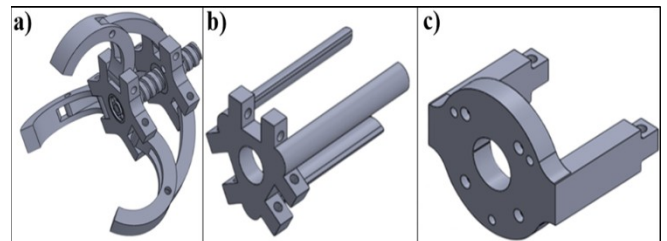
Modelo CAD inicial del gripper en SolidWorks. a) Vista isométrica del conjunto ensamblado. b) Base de acoplamiento y sistema de transmisión mediante tornillo de avance. c) Base estructural de motor.
